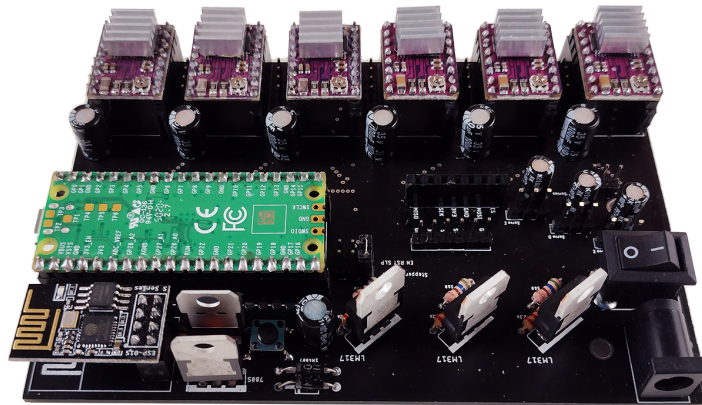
Nova placa com componentes soldados e montados.
